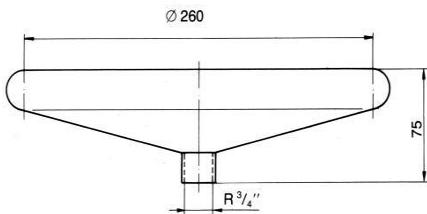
Основные габаритные и присоединительные размеры аэратора Envicon
